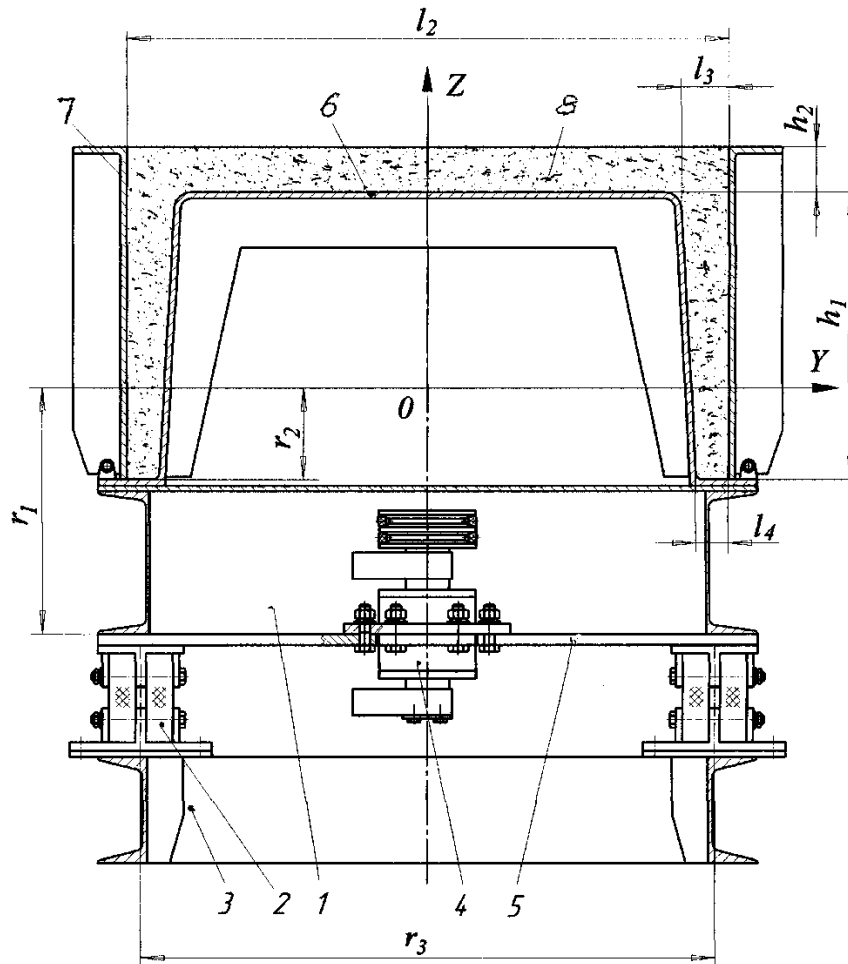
Розрахункова схема віброплощадки на стадії формування бічних стінок бетонного лотка у формі: 1 – рухома рама віброплощадки, 2 – пружна опора, 3 – опорна рама, 4 – віброзбуджувач, 5 – опорна плита, 6 – осердя форми, 7 – поздовжній борт, 8 – бетонна суміш.
